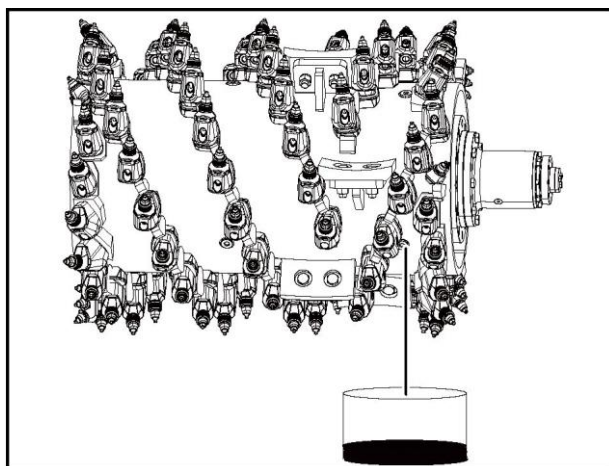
Пробка смотрового отверстия и пробка резьбового отверстия для слива масла
